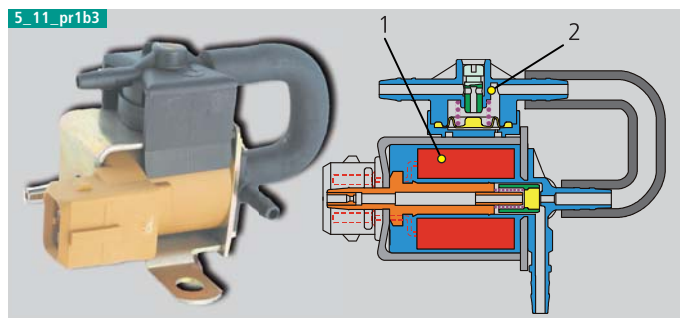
Elektrischer Druckwandler. 1 Elektromagnetventil; 2 Druckbegrenzer.
